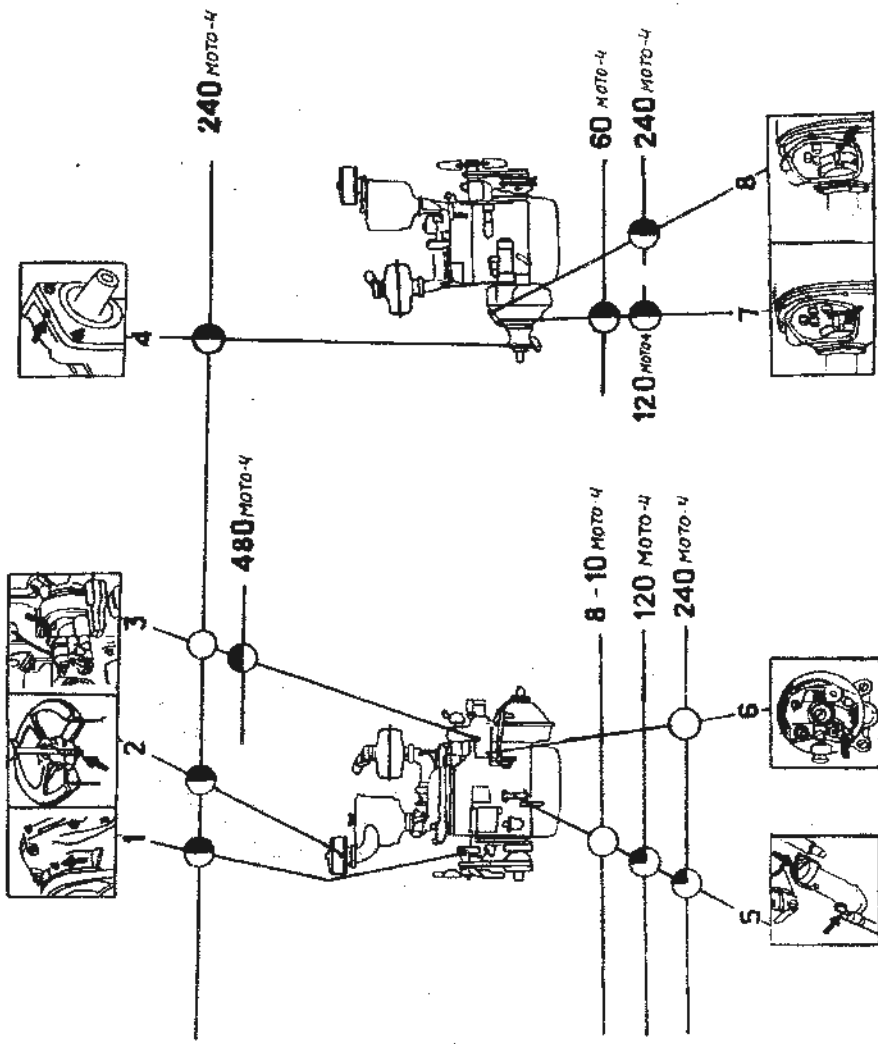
Схема смазки дизеля СМД-22. Условные обозначения
